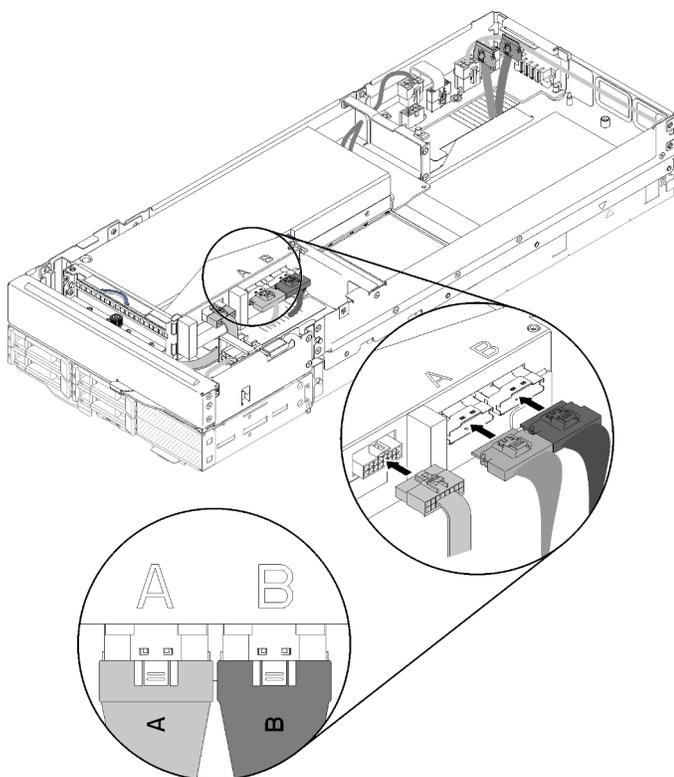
Conectando o PCIe#3-A, PCIe#4-B e o cabo diverso da placa riser ao conjunto da placa riser frontal.
